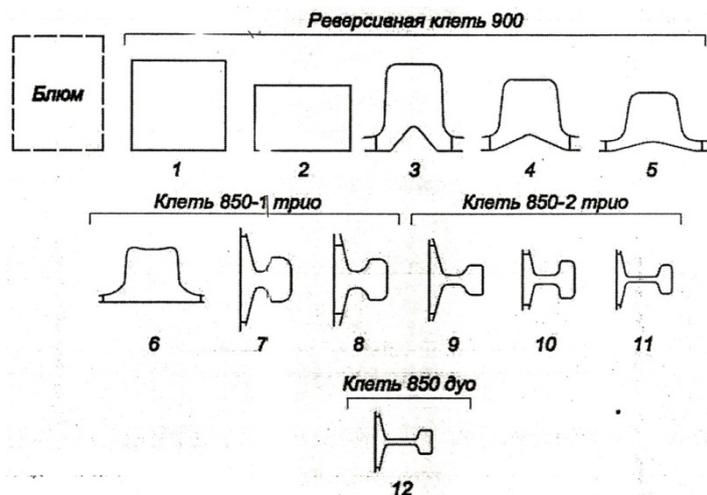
Калибровка валков для прокатки рельсов (1..12 –номера пропусков)
